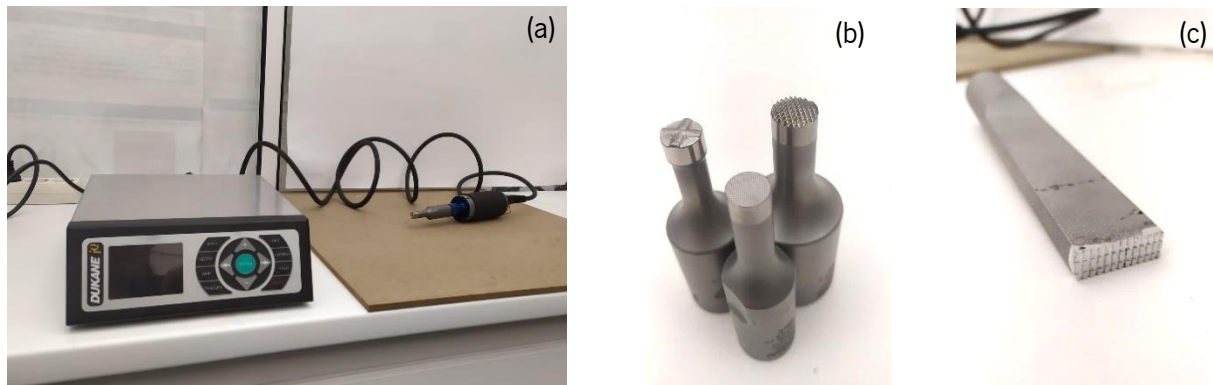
a) iQ Series Hand Held Ultrasonic Welding Systems; b) Sonotrodos forma em degrau; c) Sonotrodo lado reto
